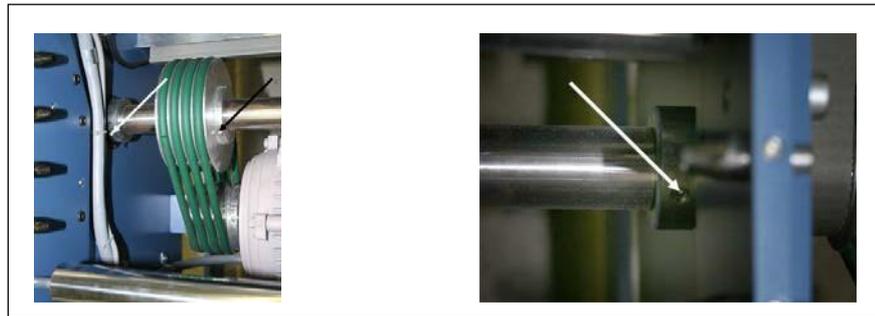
Antrieb mit Rundriemen und Antriebswelle
